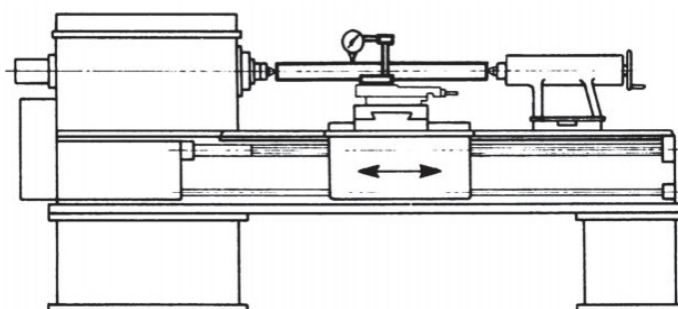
Tolerance rovnoběžnosti [30]
